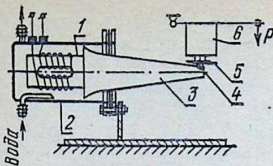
Схема установки для точечной сварки ультразвуком:
